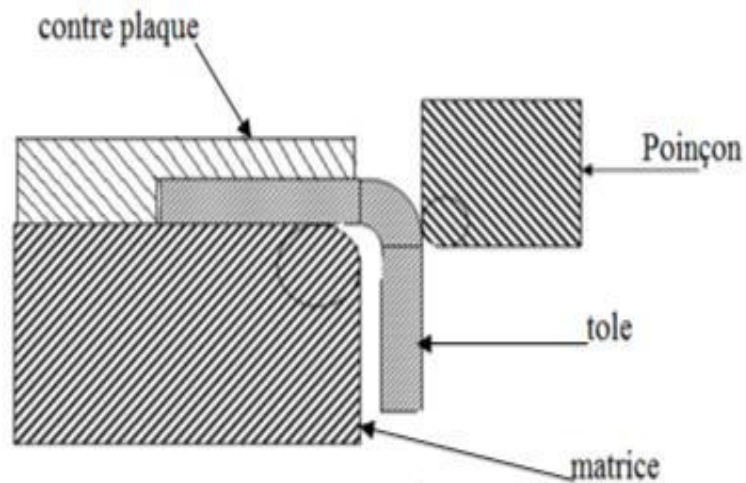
Exemple d'Outil de Cambrage en Équerre.
